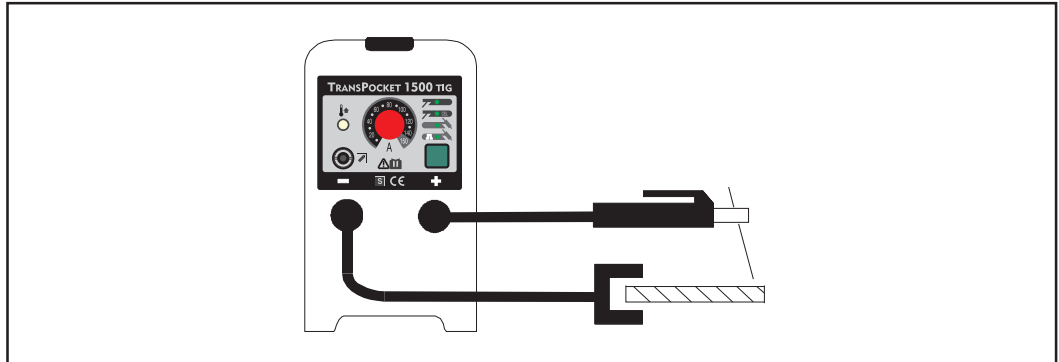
TP 1500 équipé pour le soudage à la baguette
